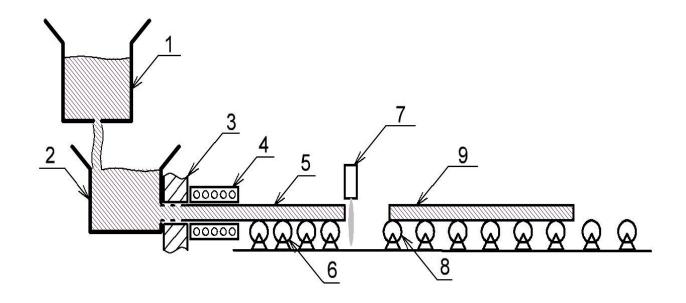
Схема технологического процесса и расположение механизмов в машине непрерывного литья заготовок: 1 — разливочный ковш;
